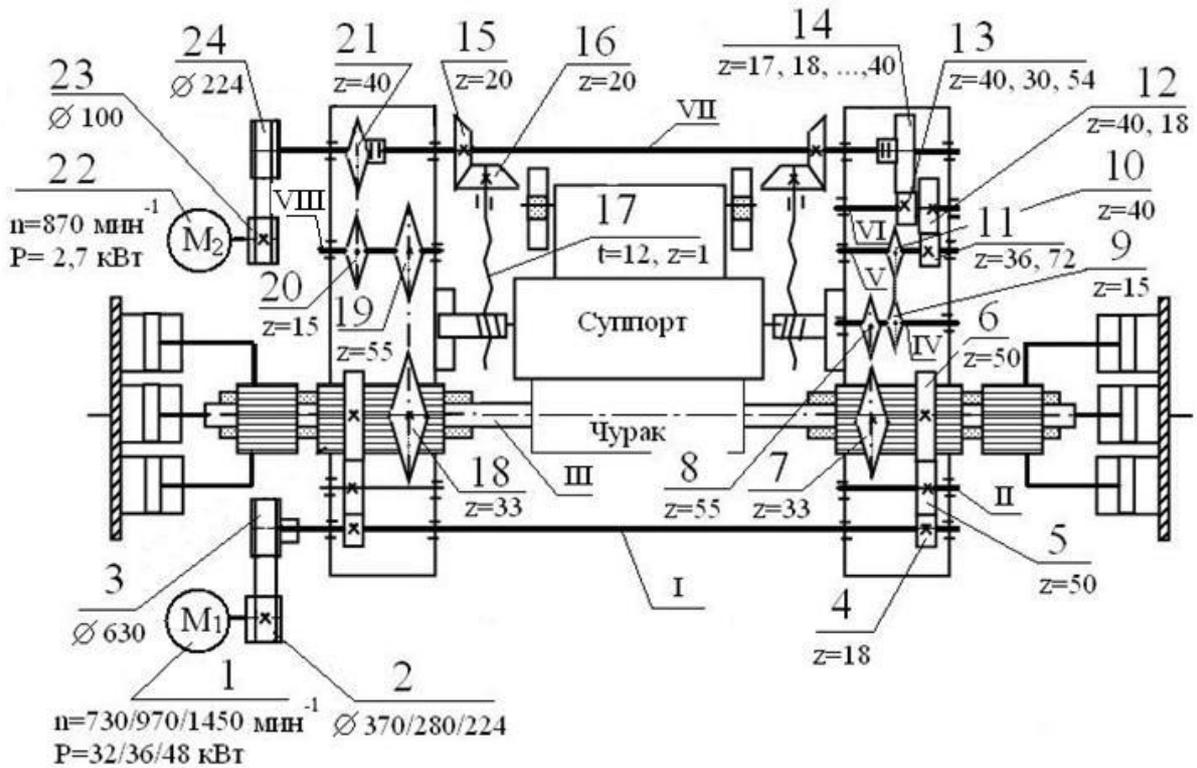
Кинематическая схема лущильного станка ЛУ17-10
